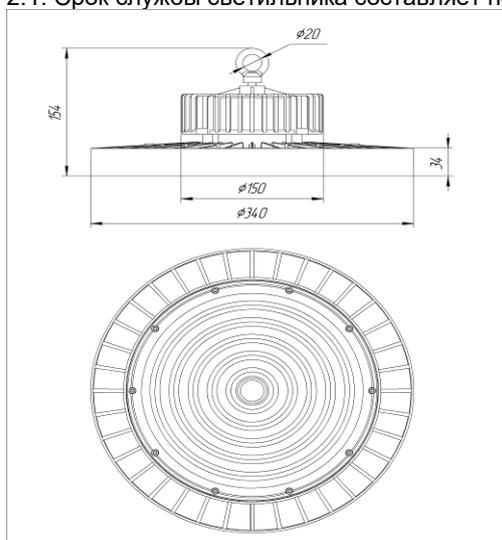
Габаритный чертеж светильника Ecomex Ray 160-180
